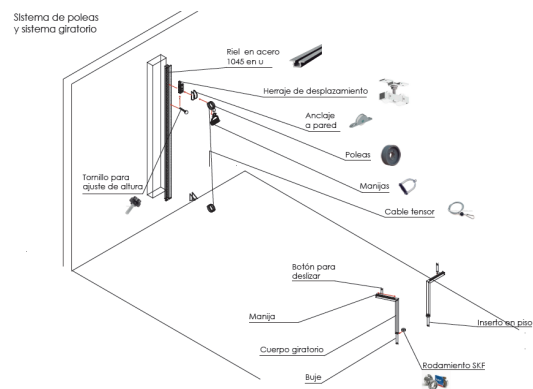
Detalle constructivo Sistema giratorio y de poleas. Auoría propia. Pág: 93
